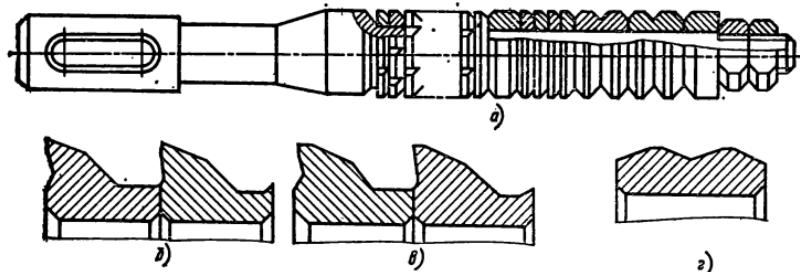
Твердосплавная режуще-выглаживающая протяжка для обработки стальных закаленных заготовок:
